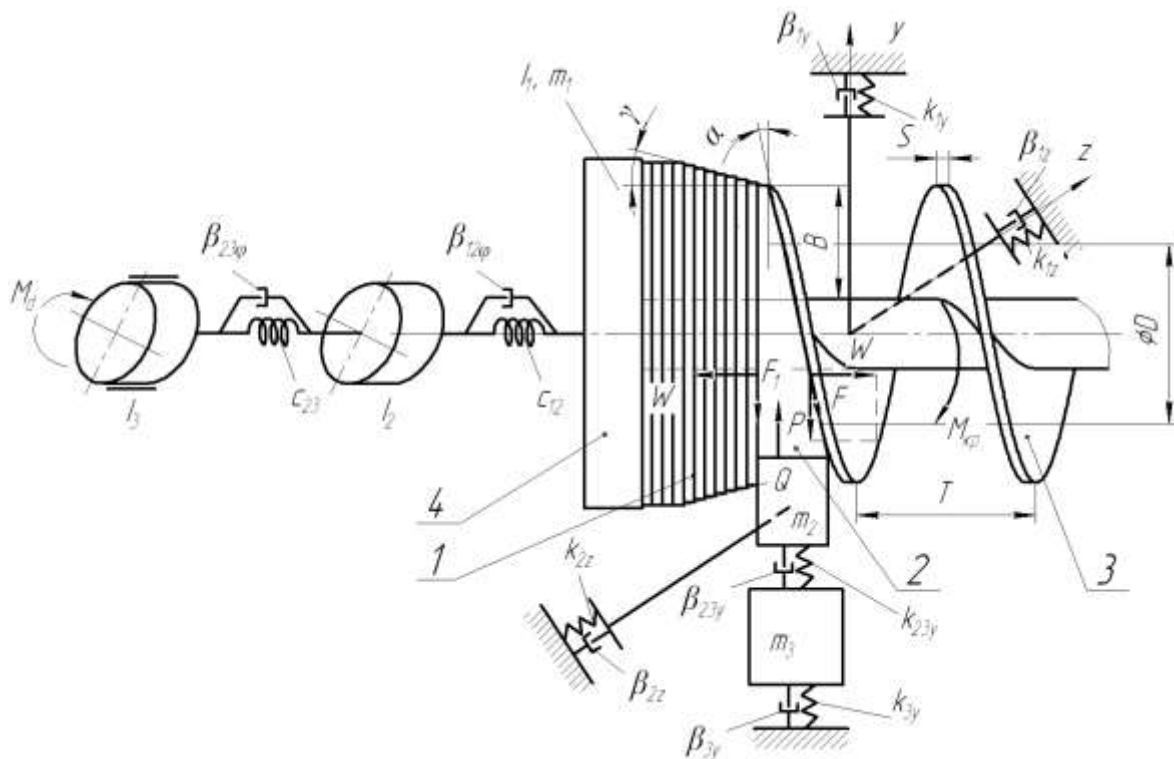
Розрахункова схема процесу калібрування витка конічної гвинтової заготовки на крок: 1 - щільно навита конічна заготовка, 2 - клин; 3 - калібровані на крок T витки гвинтової заготовки; 4 - оправка для калібрування
